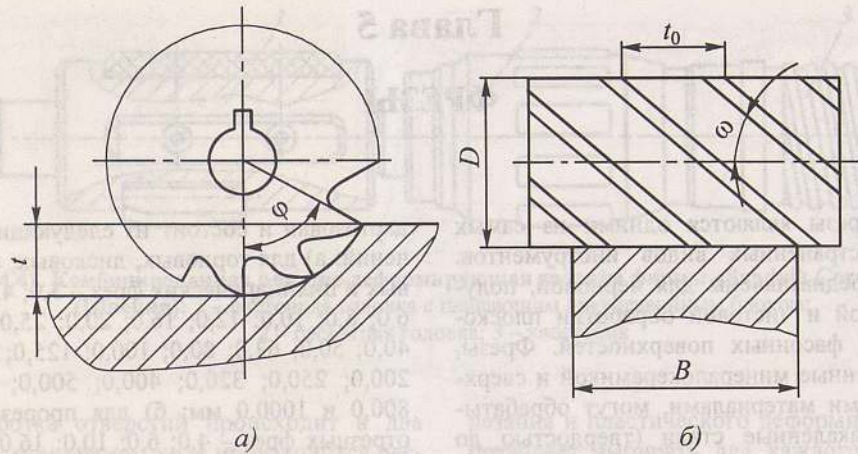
Схема фрезерования цилиндрическими фрезами:
